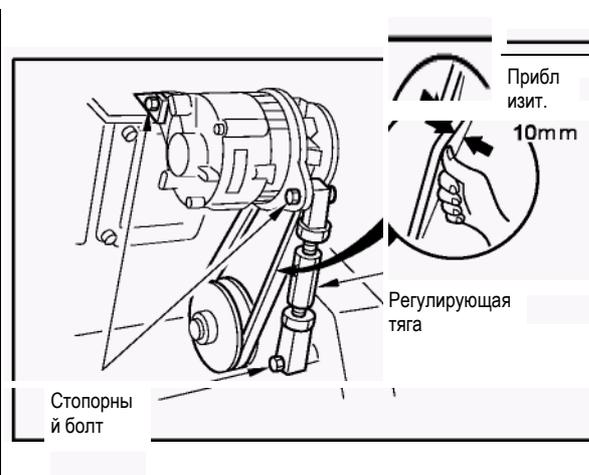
Проверка клиновидного приводного ремня и регулировка натяжения ремня
